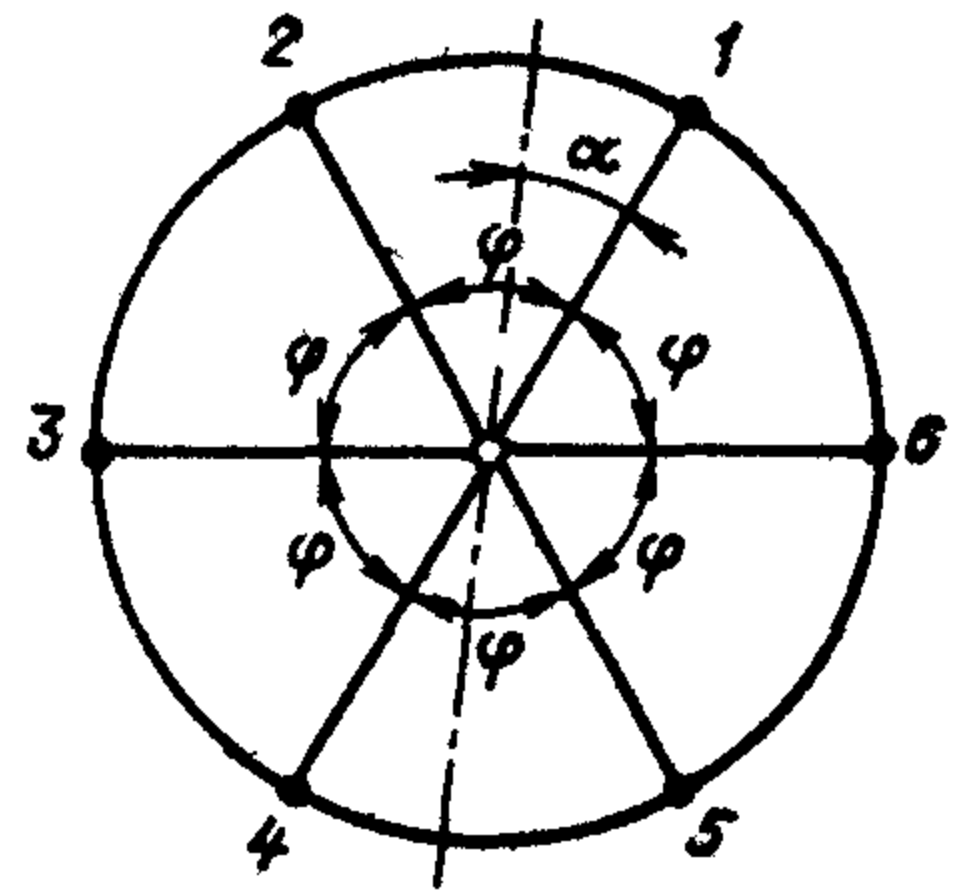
Схема расположения кривошипов шестицилиндрового четырехтактного двигателя
